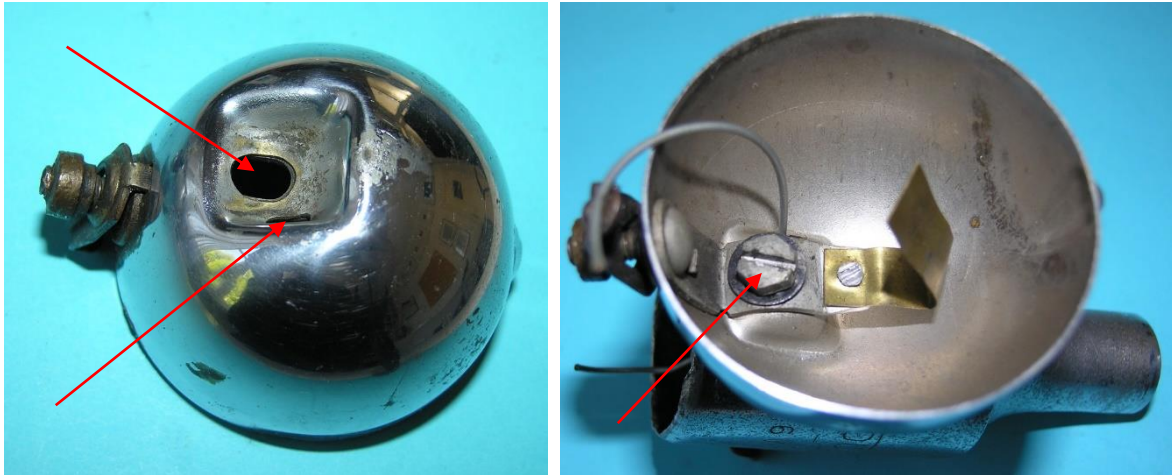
Angegossener Sockel für die Lampe: a) Position des Sockels am Gehäuse, b) Gewindebohrung zur Befestigung des Lampenkörpers, c) Durchführung des Lampenkabels
